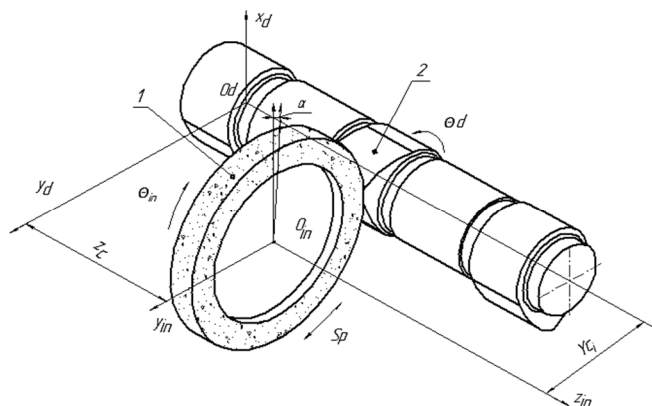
Схема шліфування розподільного вала фірмою Junker
